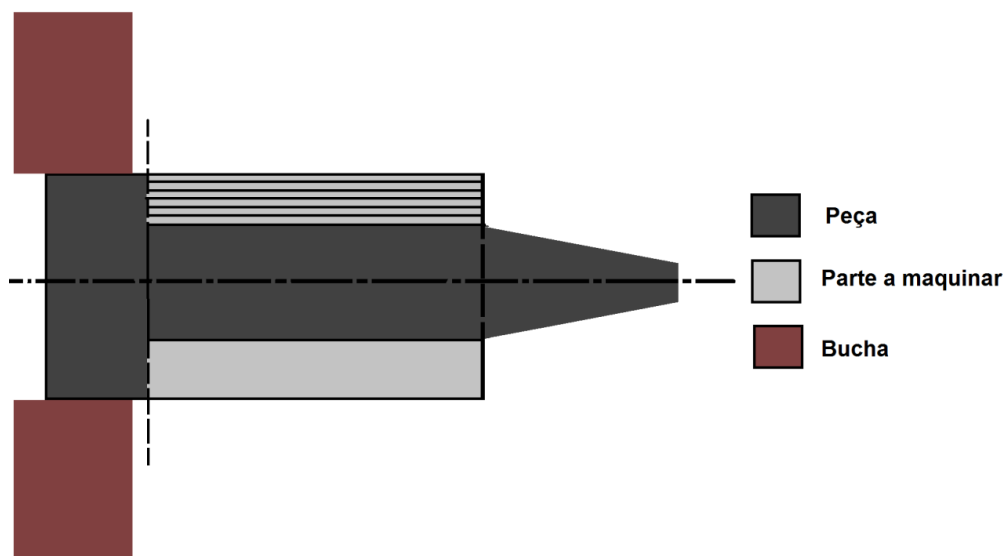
Segunda parte da maquinagem, desbaste do corpo.
